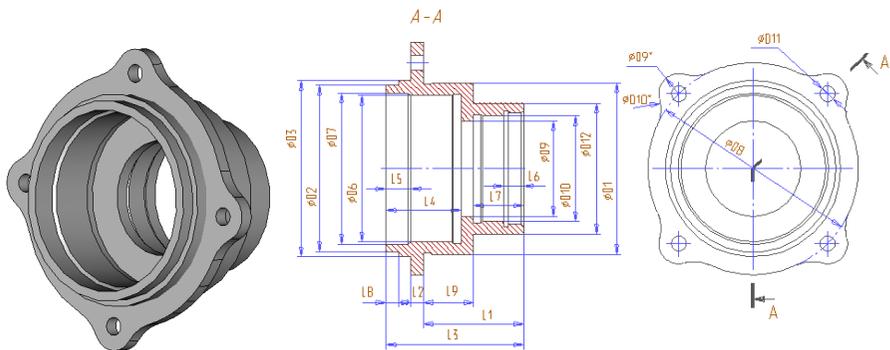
3D модель и чертёж комплексного представителя стакана подшипника
